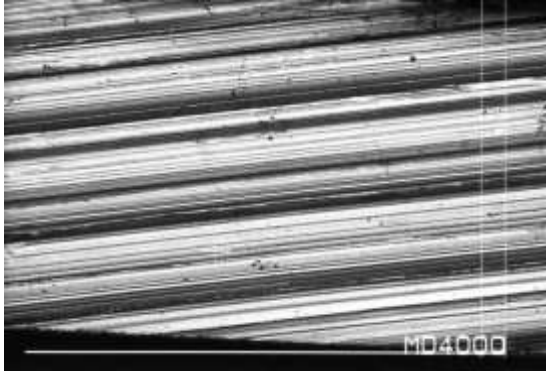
a. Das Gewinde des Messing -Teils nach einseitiger Ultraschalleinwirkung.
